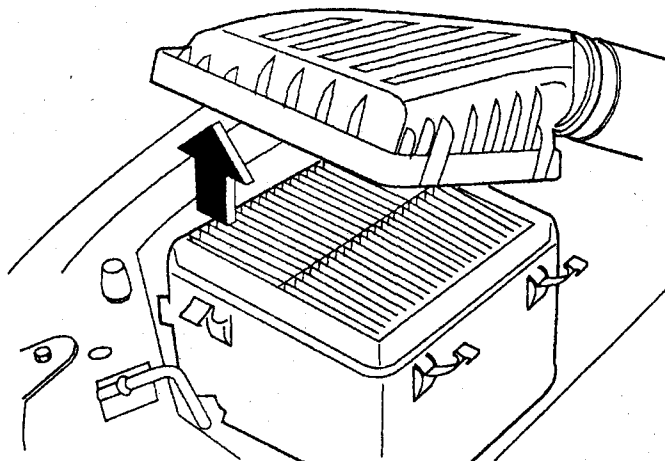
Установка воздушного фильтра двигателя MeMZ-3071 (1.3 L): 1 – корпус воздушного фильтра; 2 – фильтрующий элемент; 3 – крышка; 4 – защёлки крышки
